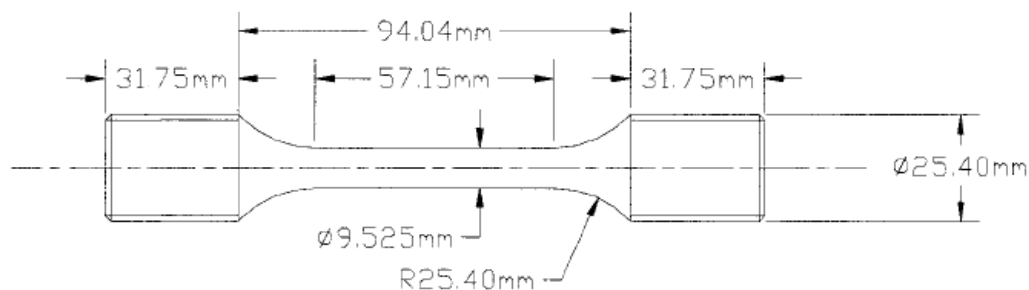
Géométrie de l'éprouvette de traction cylindrique
